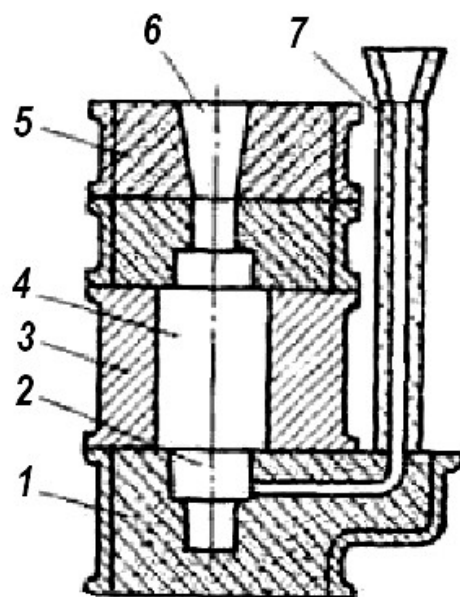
Комбинированная форма для отливки листопрокатного валка с отбеленным слоем: 1 — нижняя песчаная полуформа шейки; 2 — шейка валка; 3 — цилиндрический кокиль бочки валка; 4 — бочка валка; 5 — верхняя песчаная полуформа; 6 — прибыль; 7 — стояк
